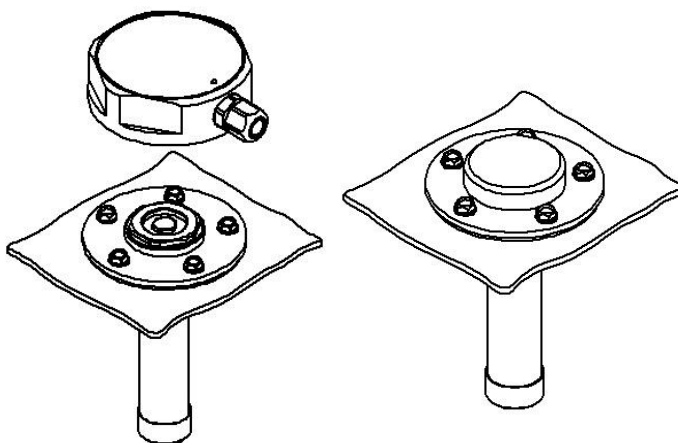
Частичный демонтаж датчика уровня топлива и установка крышки-заглушки
